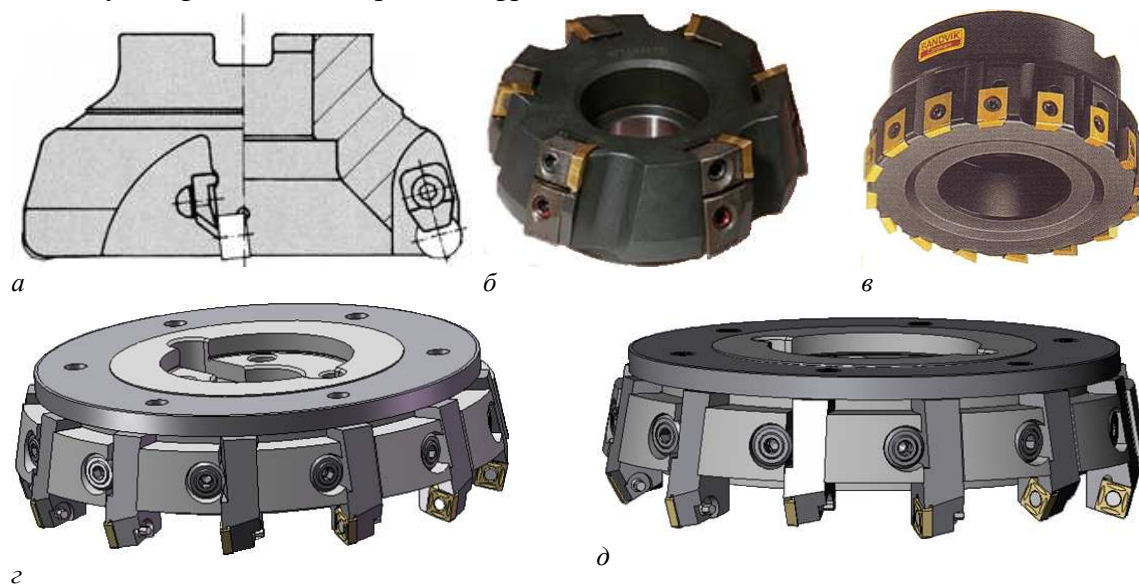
Пропоновані варіанти конструкції торцевих фрез для технологічних ніш при обробці вуглецевих сталей: а – фреза Kennametal Hertel R232 для чистової обробки; б – фреза Pramet W75SP15D з можливістю регулювання в осьовому напрямку; в – фреза з тангенційним розташуванням багатограних пластин SANDVIK Coromant T-Line; г – фреза касетна  $\varphi=75^0$  «Касета 1»; д – фреза з діленням зрізу по ширині і товщині «Касета 2»
